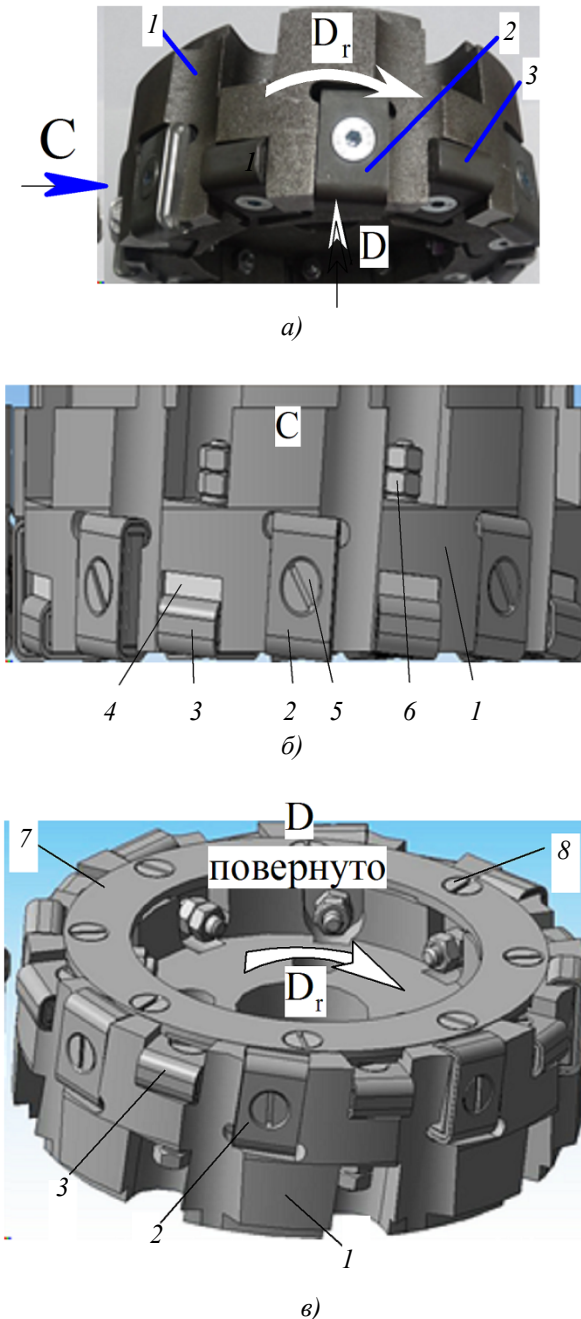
Реальная модель комбинированной торцевой фрезы со взаимно перпендикулярными рядами твердосплавных режущих пластин:
